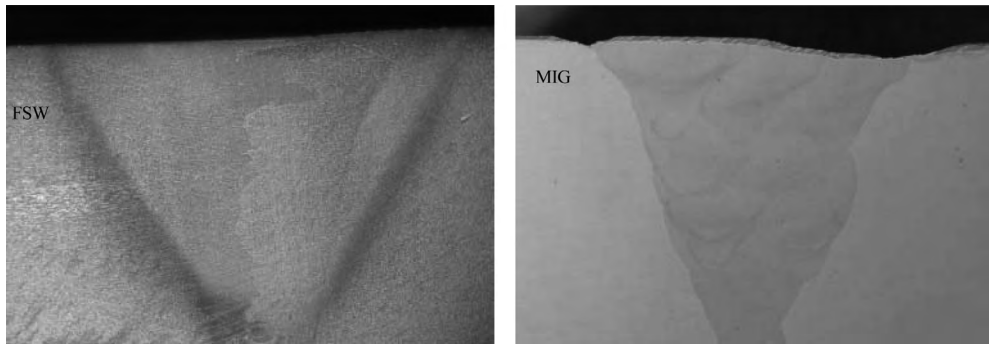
FSW 和 MIG 焊接接头低倍形貌
